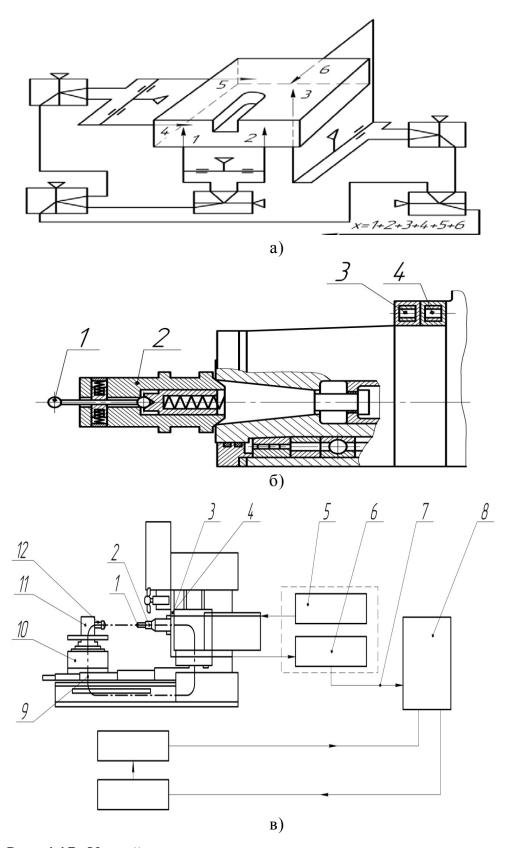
Устройства для автоматического контроля положения заготовки в приспособлении: 1- шуп; 2- датчик; 3,4- трансформаторы; 5- генератор; 6- формирователь; 7- канал; 8- разъем; 9- виток; 10- спутник; 11- заготовка; 12- поверхность касания
